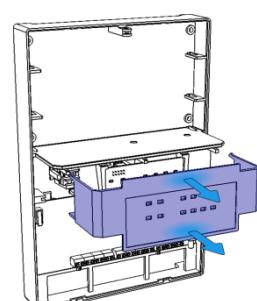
Демонтаж корпуса контроллера (шаг 3)
